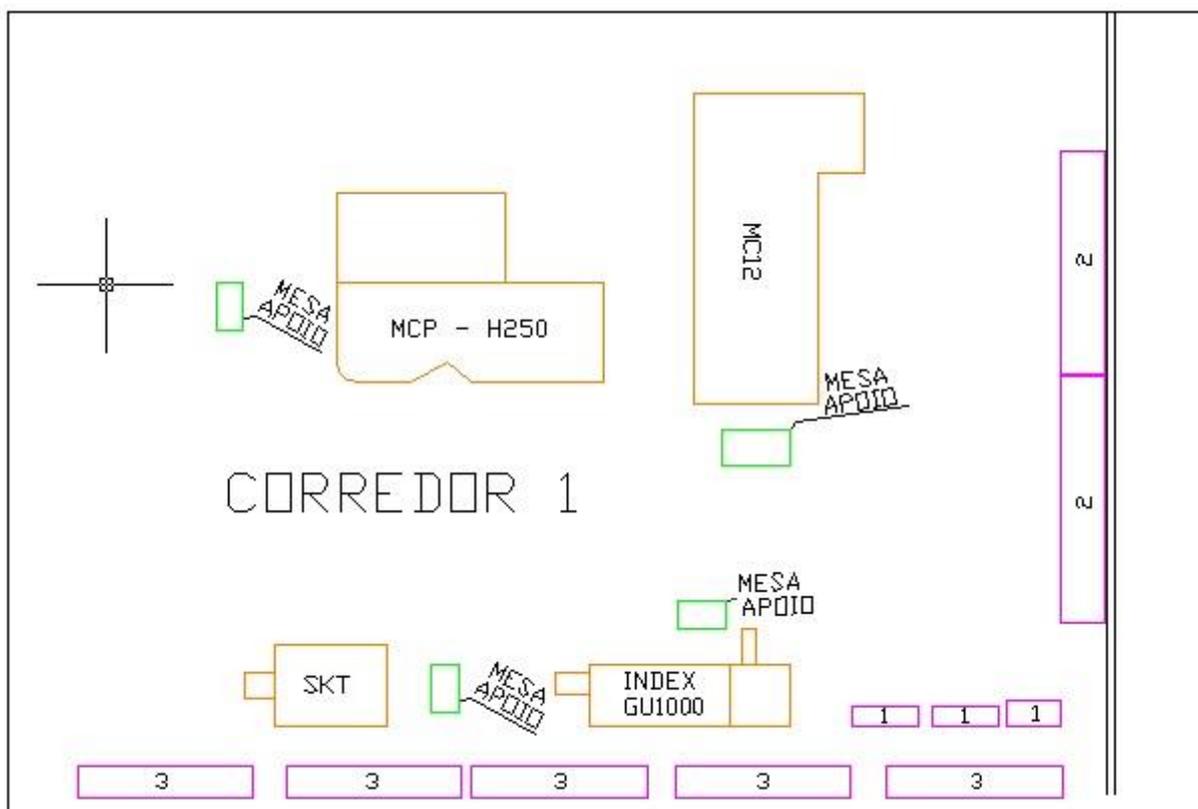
Planta baixa da proposta de novo *layout*. Fonte: o autor.
